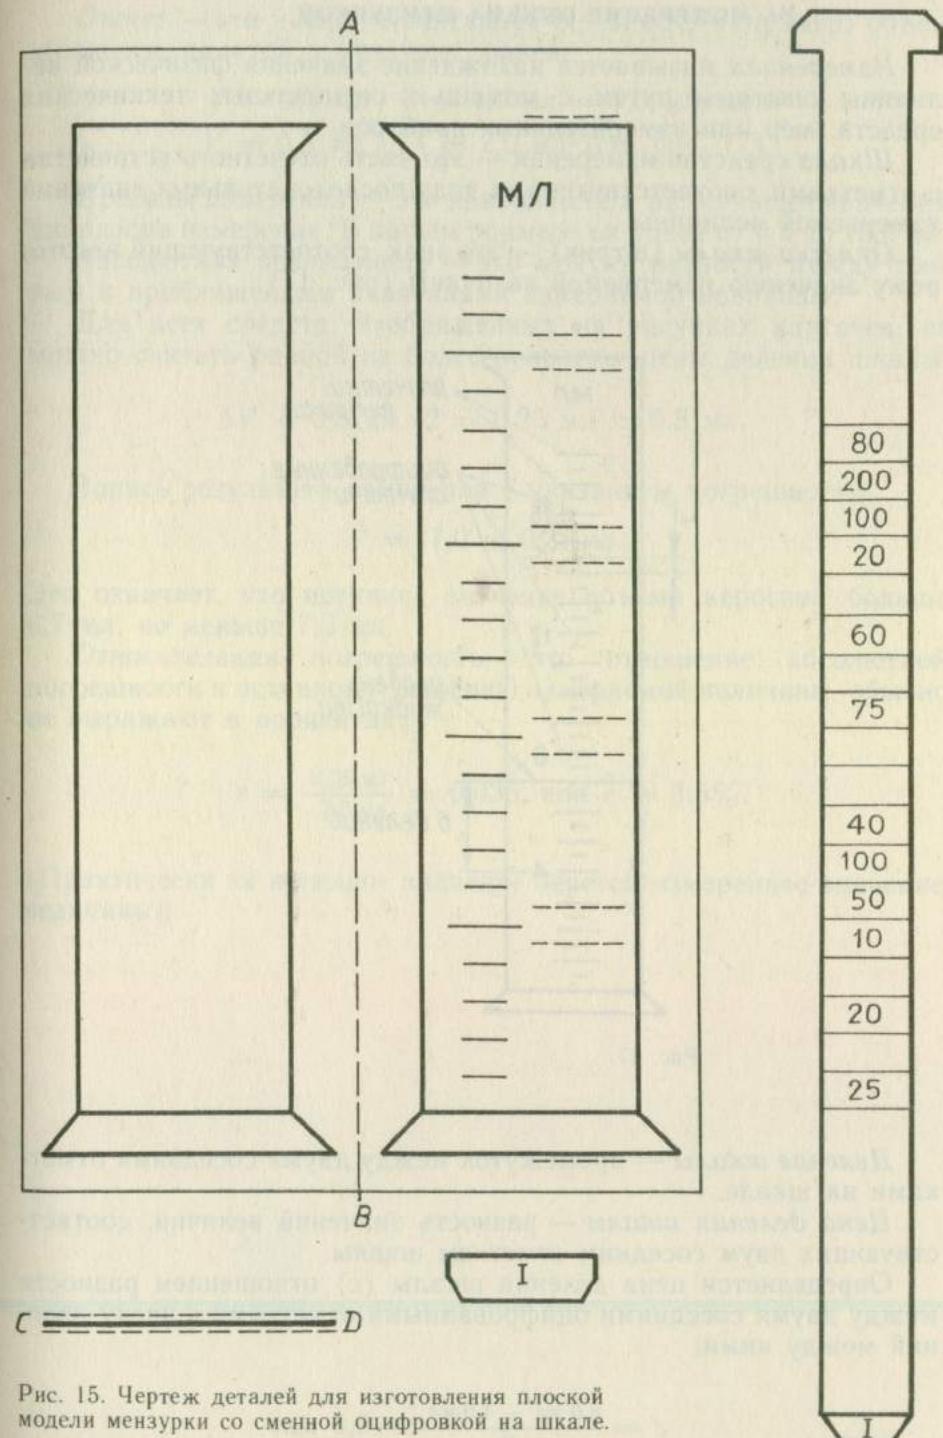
Чертеж деталей для изготовления плоской модели мензурки со сменной оцифровкой на шкале.
